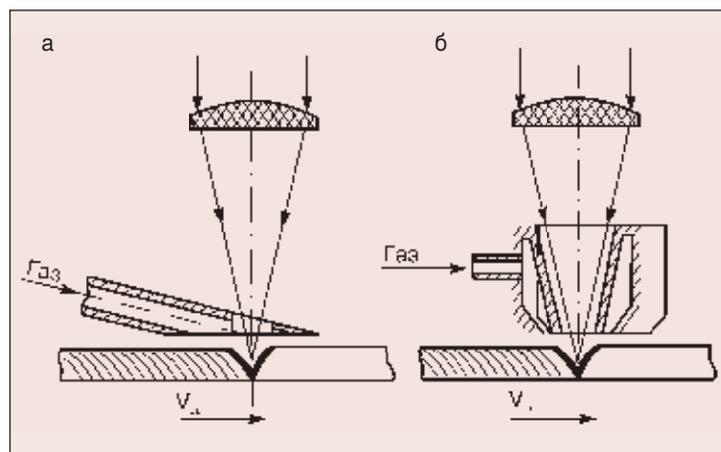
Схема лазерной сварки: а — с медной трубкой; б — с коническим соплом
